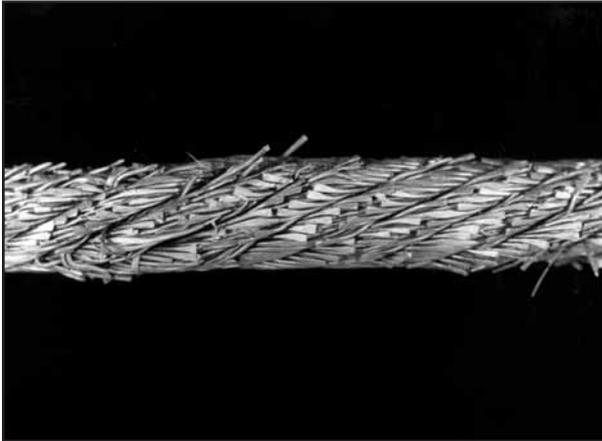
Dieses Seil hat in einer zu engen Seilscheibe gearbeitet.
